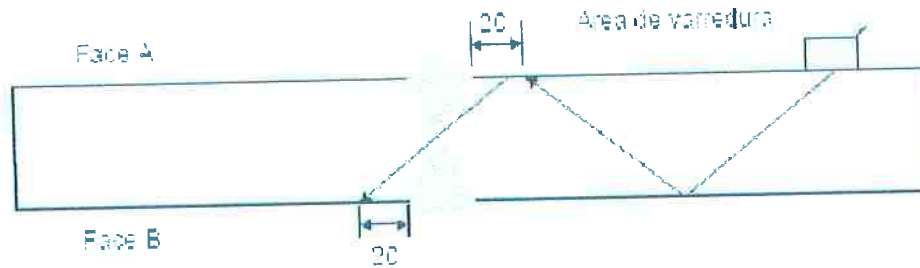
Técnica geral para inspeção de soldas de topo por ultra-som (2)
